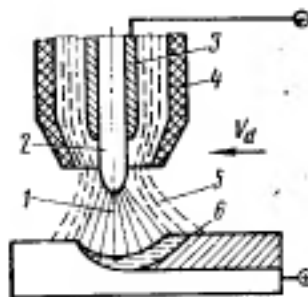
Схема сварки в атмосфере защитных газов:
